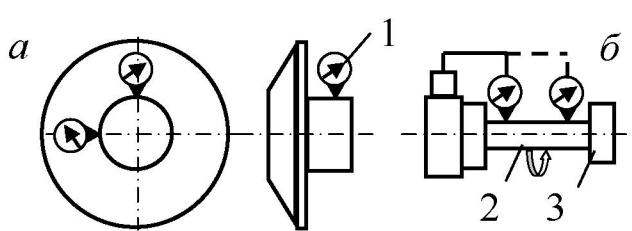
Схема измерения радиального биения пильного вала станка:
